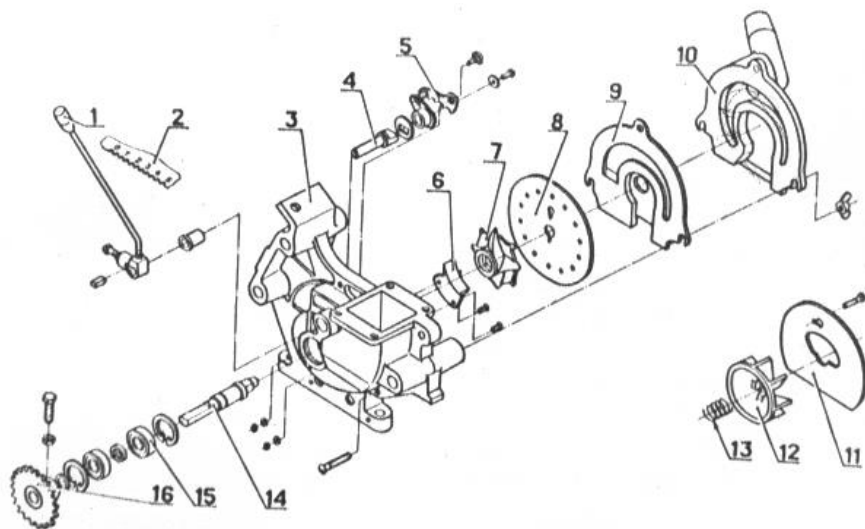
Висівний апарат сівалки СУПН-8. 1 - ричаг; 2-шкала; 3, 5, 6 - кронштейн; 4, 14 - вісь; 7 - ворошилка; 9, 11 - прокладка; 10 - кришка; 12 -активатор, 13, 16 - пружина, 15 - кільце.
